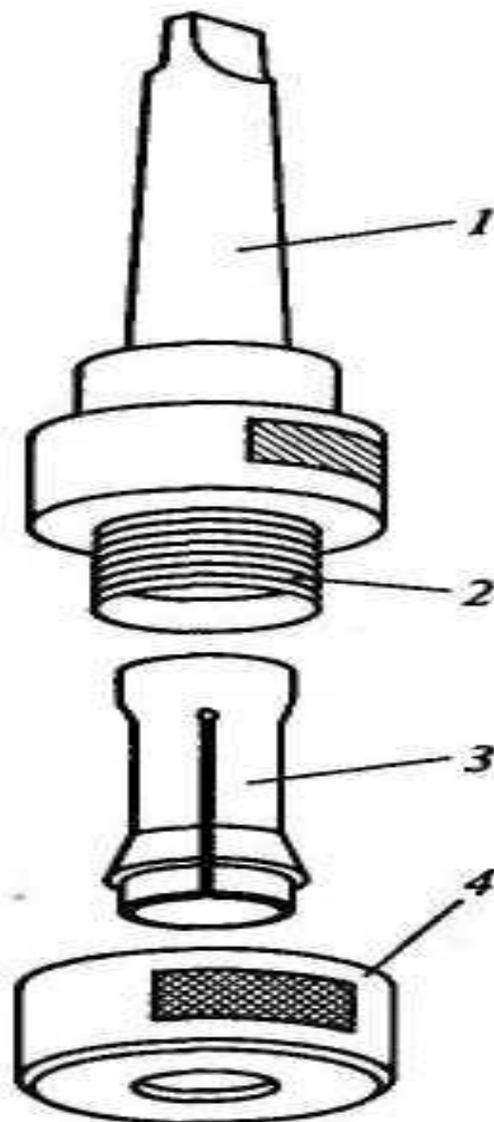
Цанговый сверлильный патрон: 1- хвостовик; 2 - цилиндрическая часть; 3 - разрезная втулка; 4 – кольцо
